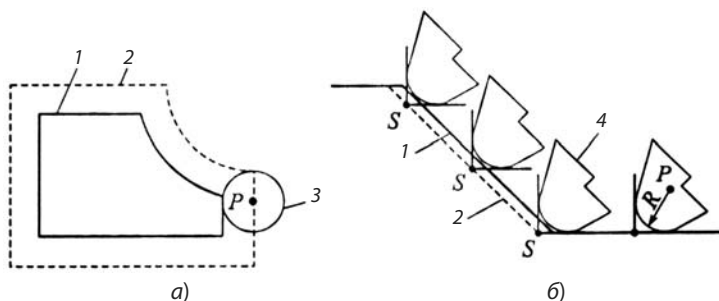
Движение настроенной точки P при фрезеровании (а) и точении (б): 1 — обрабатываемый контур; 2 — движение центра инструмента; 3 — фреза; 4 — резец
